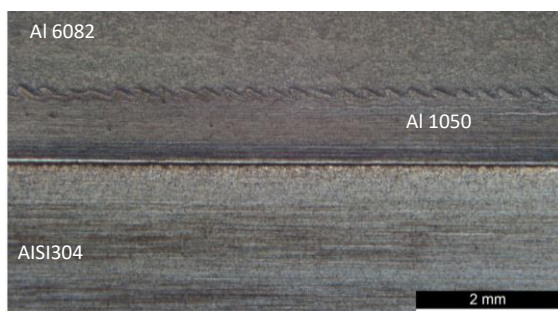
Macrografia das interfaces da soldadura Al-Al-AISI304.
